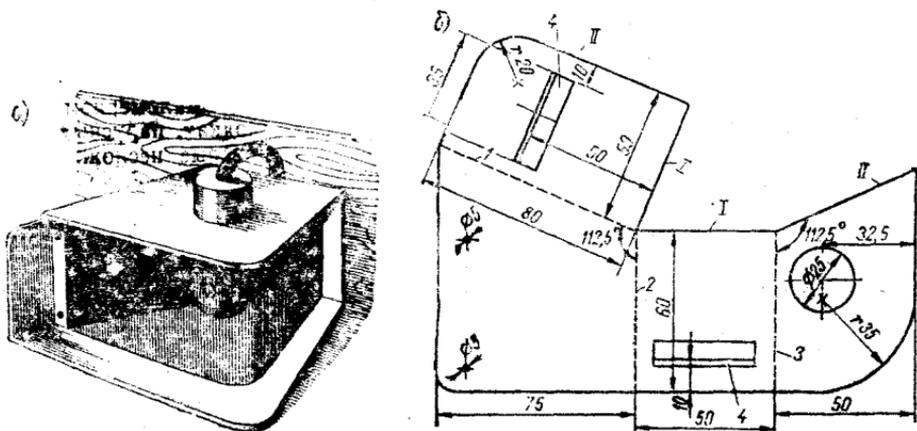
Самодельный бортовой отличительный огонь: а — фонарь в сборе; б — развертка корпуса.
